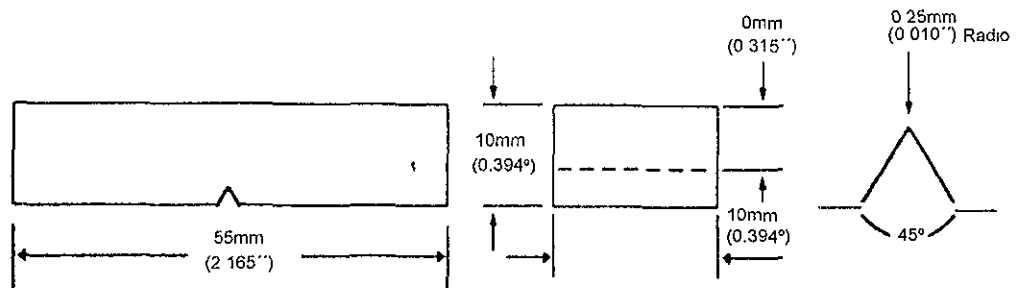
Dimensiones de la probeta de impacto del tipo en "V"
